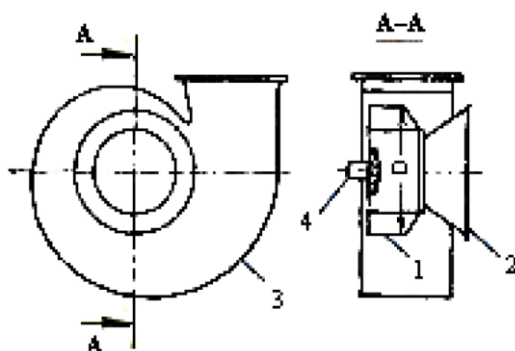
Общий вид и конструктивная схема одноколесного центробежного вентилятора: 1 – рабочее колесо; 2 – приемный патрубок; 3 – спиральный отводящий канал; 4 – вал электродвигателя
